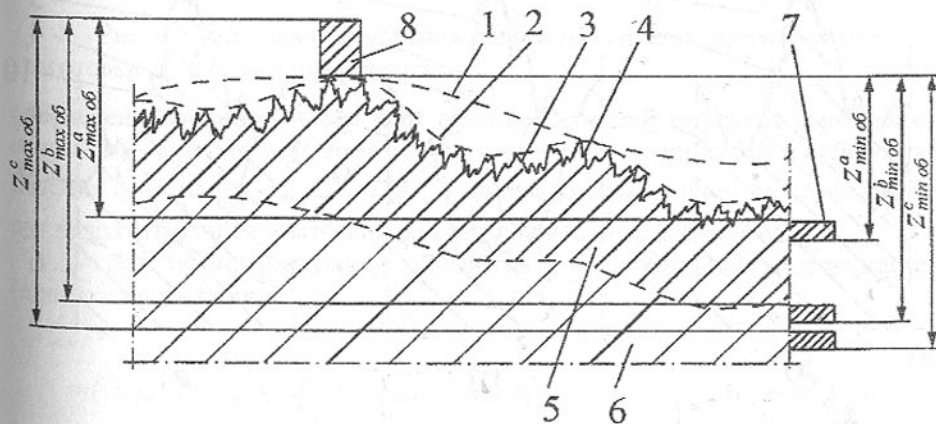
Схема поверхностного слоя заготовки и варианты расположения допусков изделия
